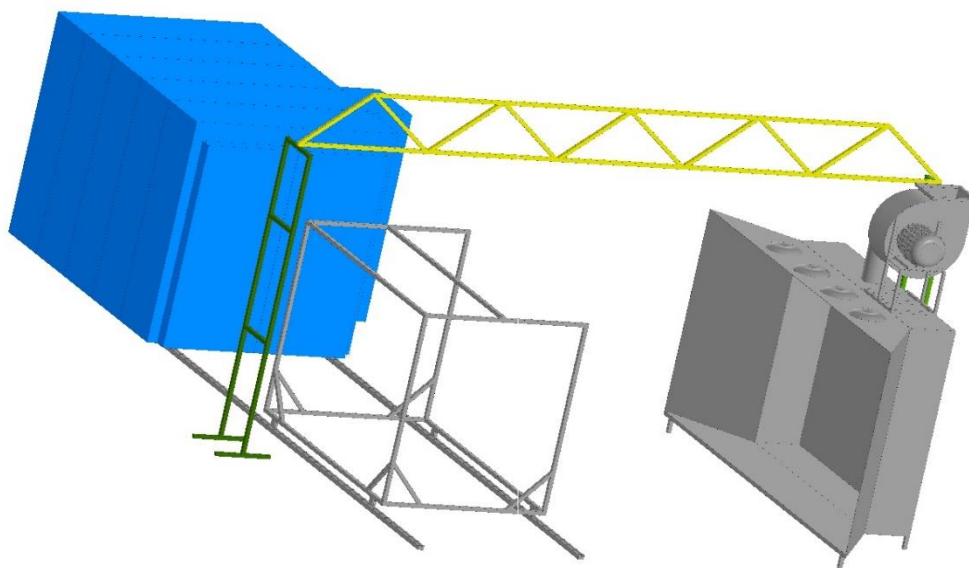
Установка для нанесения лакокрасочных покрытий
